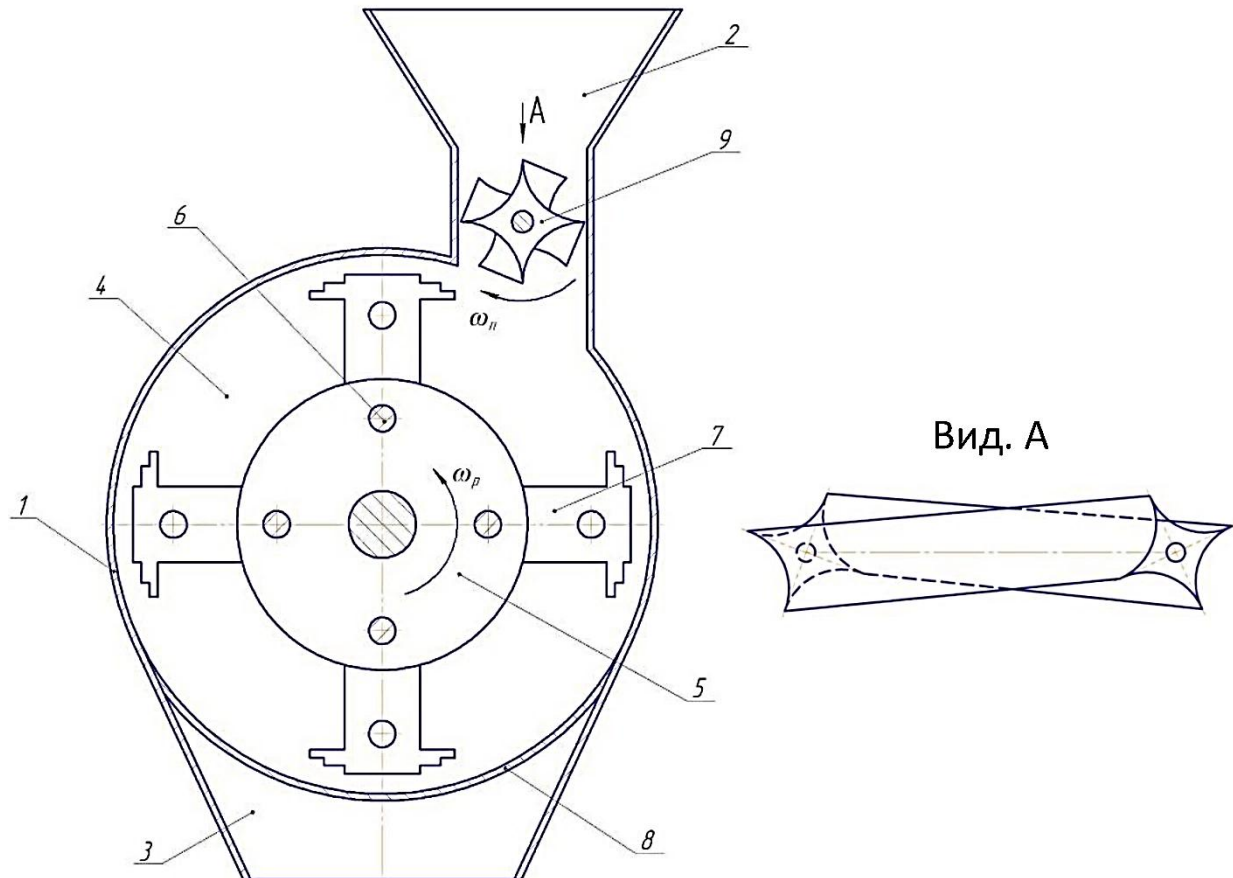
Молоткова дробарка: 1 – циліндричний корпус; 2 – завантажувальний бункер; 3 – вивантажне вікно; 4 – дробильна камера; 5 – ротор; 6 – палець; 7 – молоток; 8 – решето; 9 - живильне пристрій
